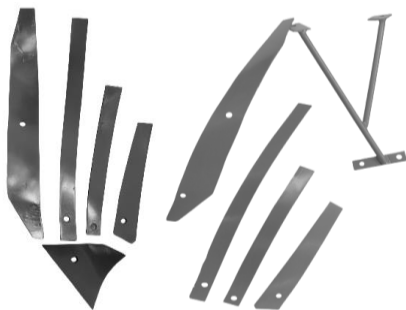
Вибрационный пластинчатый отвал корпуса плуга
